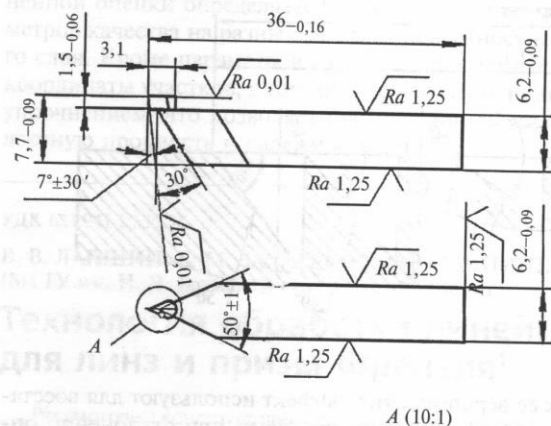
Алмазный резец для обработки негативной матрицы Френеля
